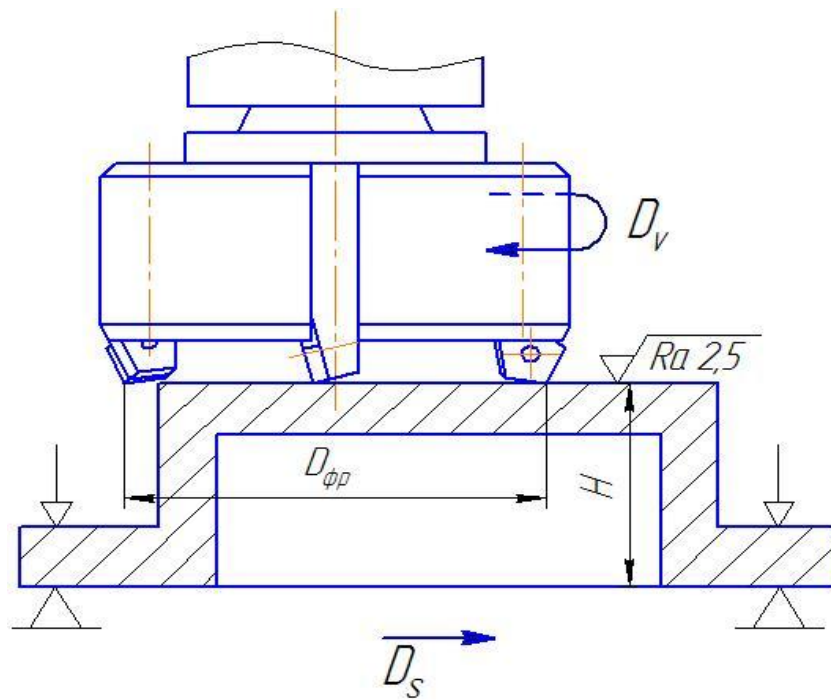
Схема обработки корпусной детали на вертикально-фрезерном станке
